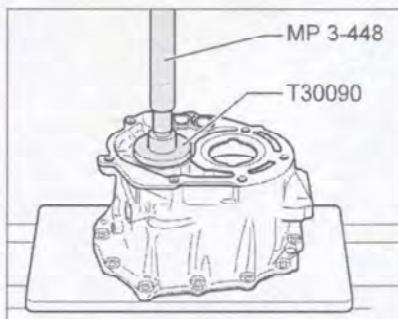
Извлечение роликоподшипника первичного вала.
